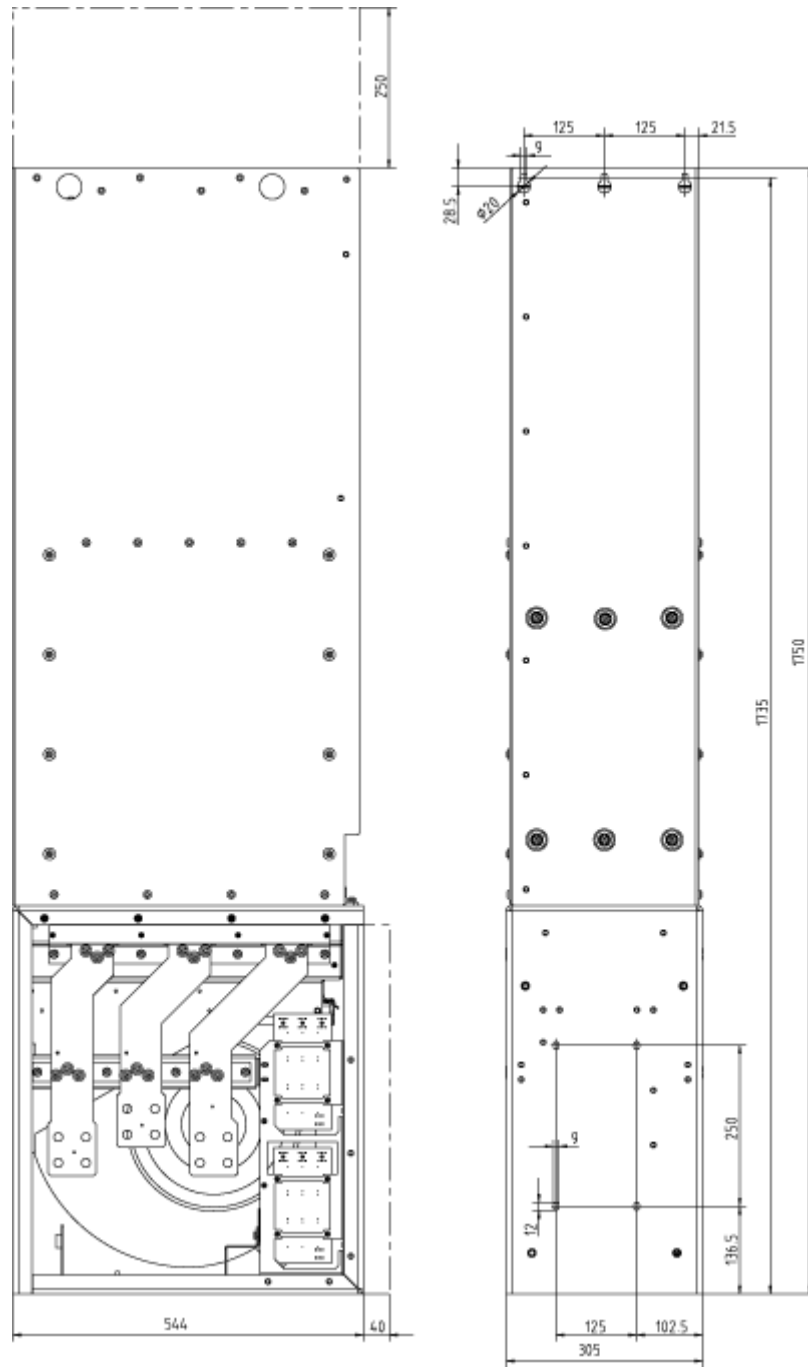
Габаритный чертеж активного интерфейсного модуля, типоразмер Н1 Вид сбоку, вид сзади
